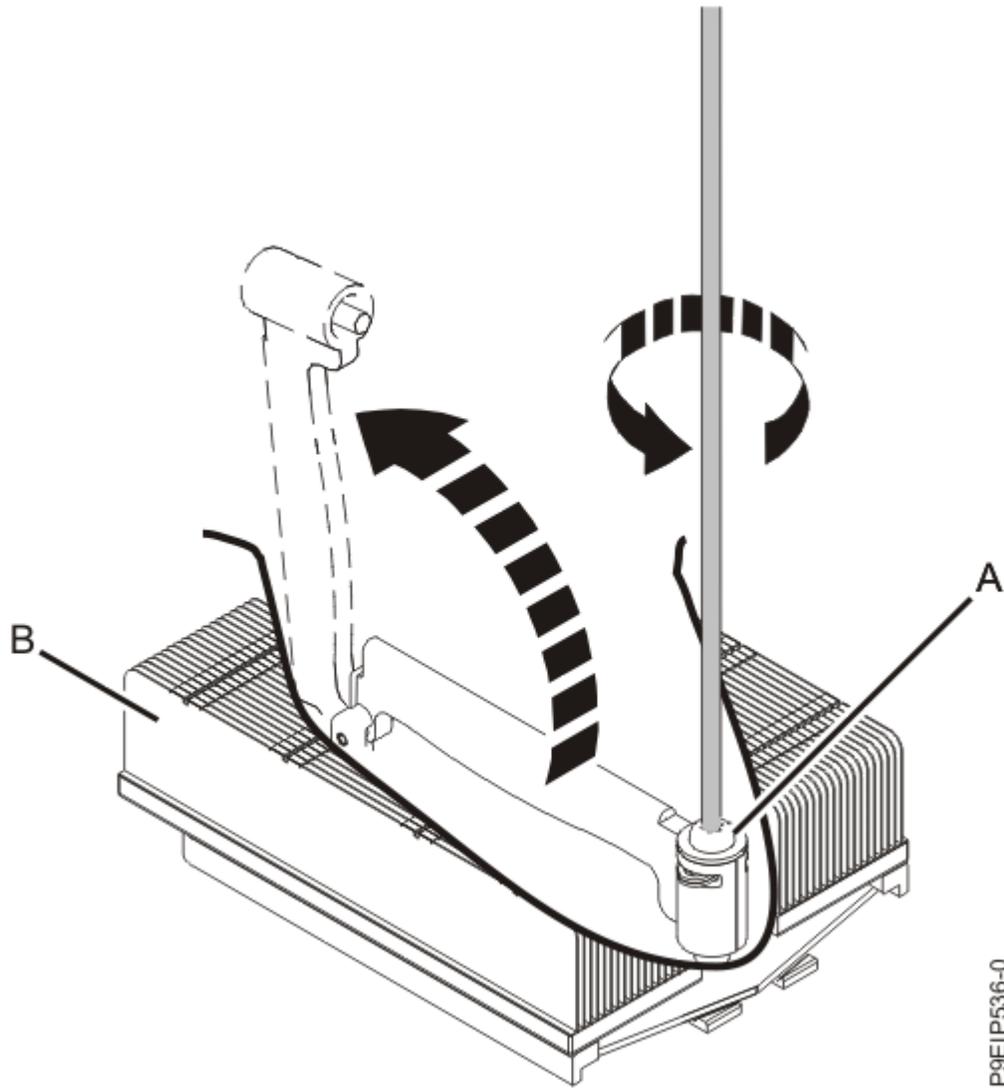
Desserrage de la vis du bras de chargement du dissipateur thermique
